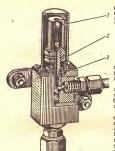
Регулировка регулятора давления: 1 — колпачок; 2 — контргайна; 3 — прокладка.
